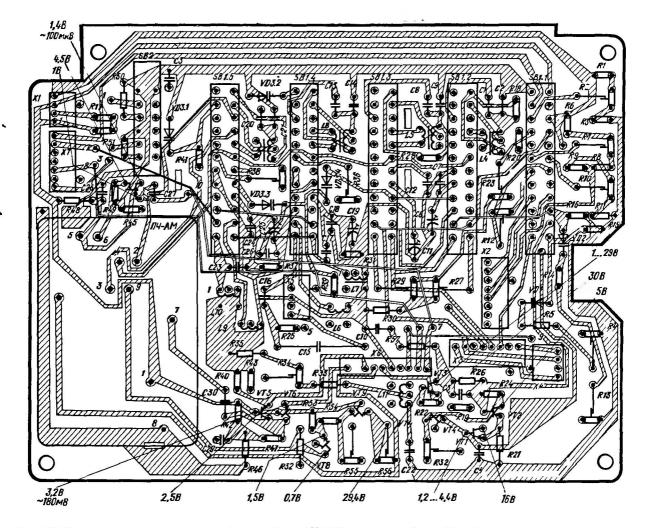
Электромонтажная схема печатиой платы блока АМ (АЗ) магнитолы «Арго РМ-006С» (вид со стороны пайки деталей)
